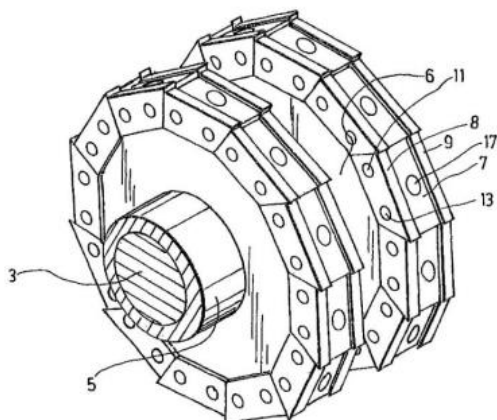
Режущий диск: 3 - ротор; 5 - разделительные распорки; 6 - носитель венца; 7 – носитель ножей 8 и 9 - ножи; 11 и 13 - винты; 17 – центральный винт
